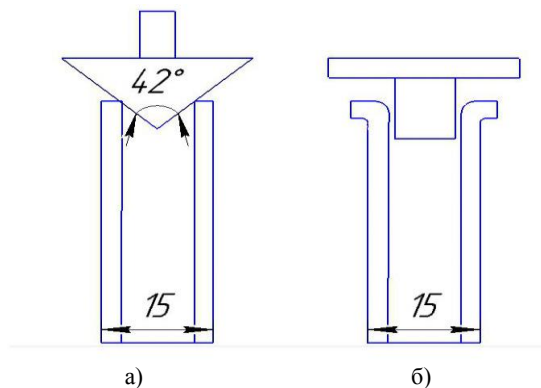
Конус і насадка: а — конус для розвальцювання;
